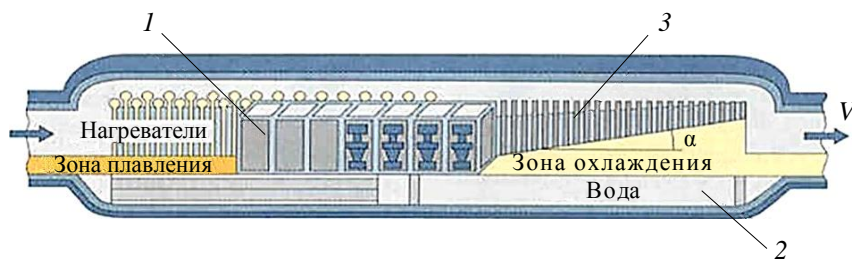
Конструкция промышленной установки ПМП-2: 1 – контейнеры с формами; 2 – охлаждаемый кристаллизатор; 3 – нагреватель печи подогрева форм
